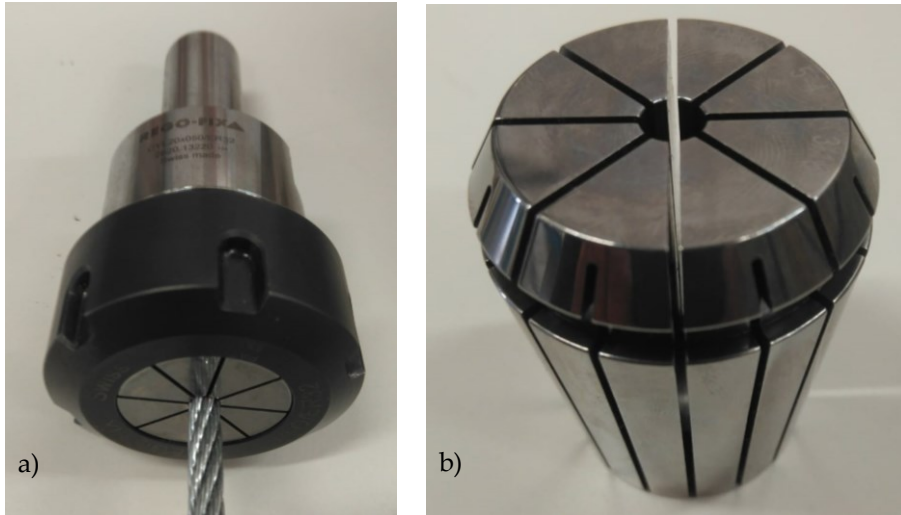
a) Portaherramientas, b) Pinza cónica.
